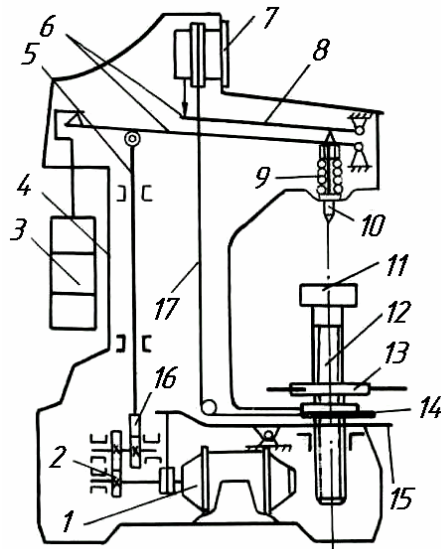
Схема пресса Роквелла: 1 – электродвигатель; 2 – червячный редуктор; 3 – грузы; 4 – корпус; 5 – шток; 6 – грузовой рычаг; 7 – индикатор; 8 – рычаг; 9 – пружина; 10 – индентор; 11 – подъёмный столик; 12, 13 – пара винт-маховик; 14 – механизм подъёмного столика; 15 – кнопка «Пуск»; 16 – кулачковый блок; 17 – трос управления индикатором
